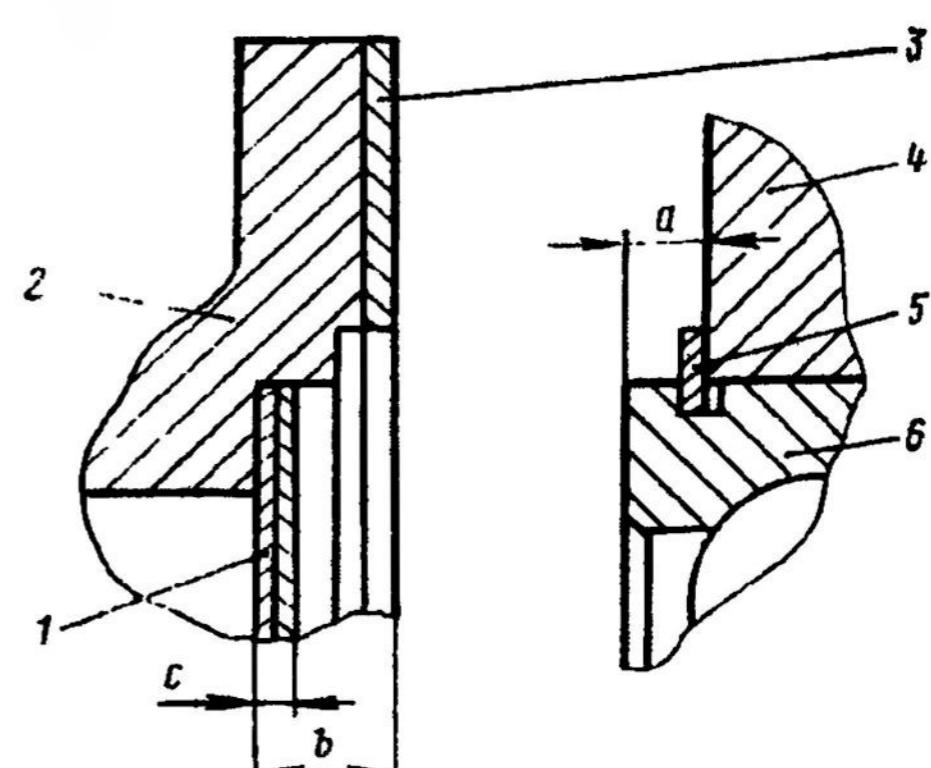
Схема замеров для регулирования осевых зазоров в подшипниках ведущего и ведомого валов:
